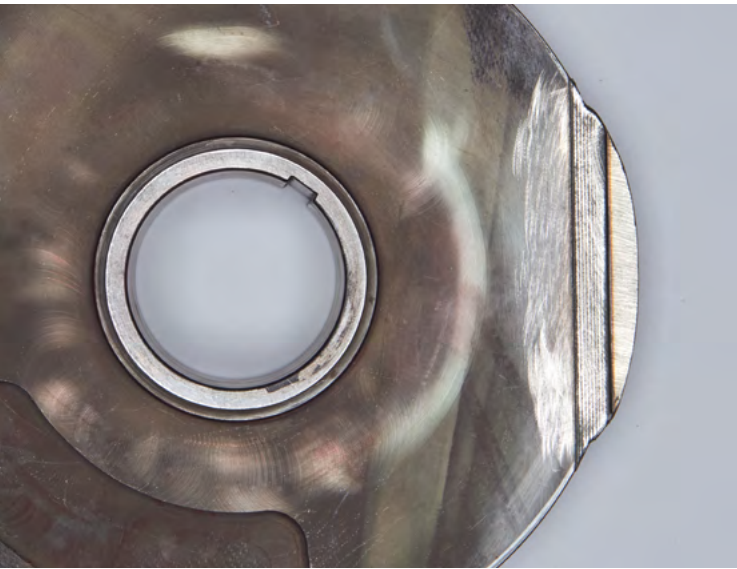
Laufwerk mit aufgeschweisstem und teilweise bearbeitetem Teil.
